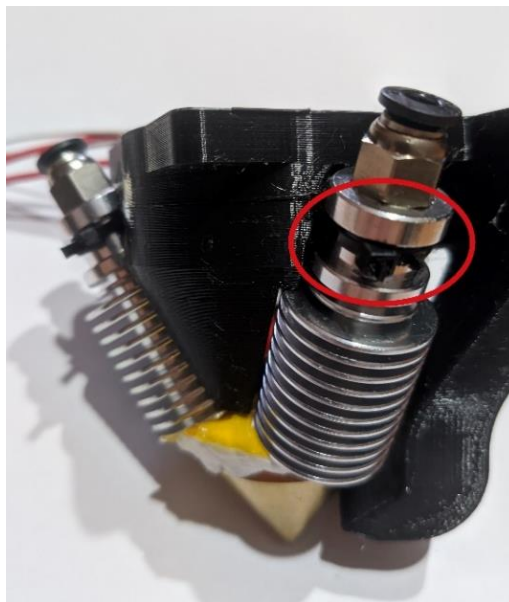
Fixação do bico extrusor ao suporte com abraçadeiras plásticas.
